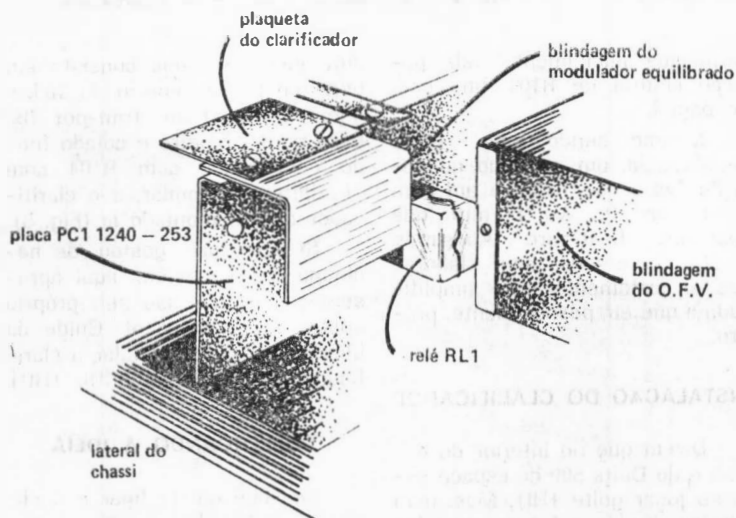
Fixação da plaqueta do clarificador na chapa "L". O equipamento é visto de frente, pelo lado esquerdo.
